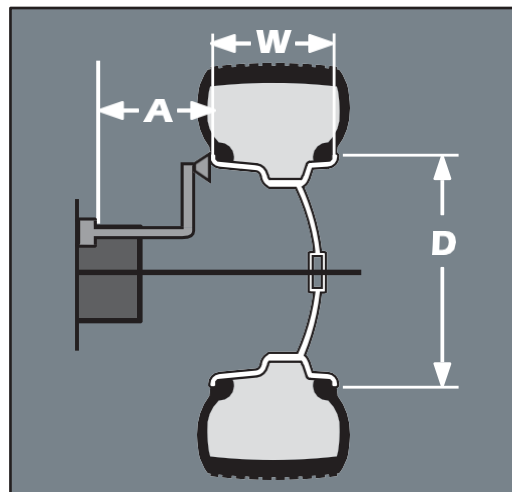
Dimensions des pneus A, W et D (écart, largeur et diamètre)
